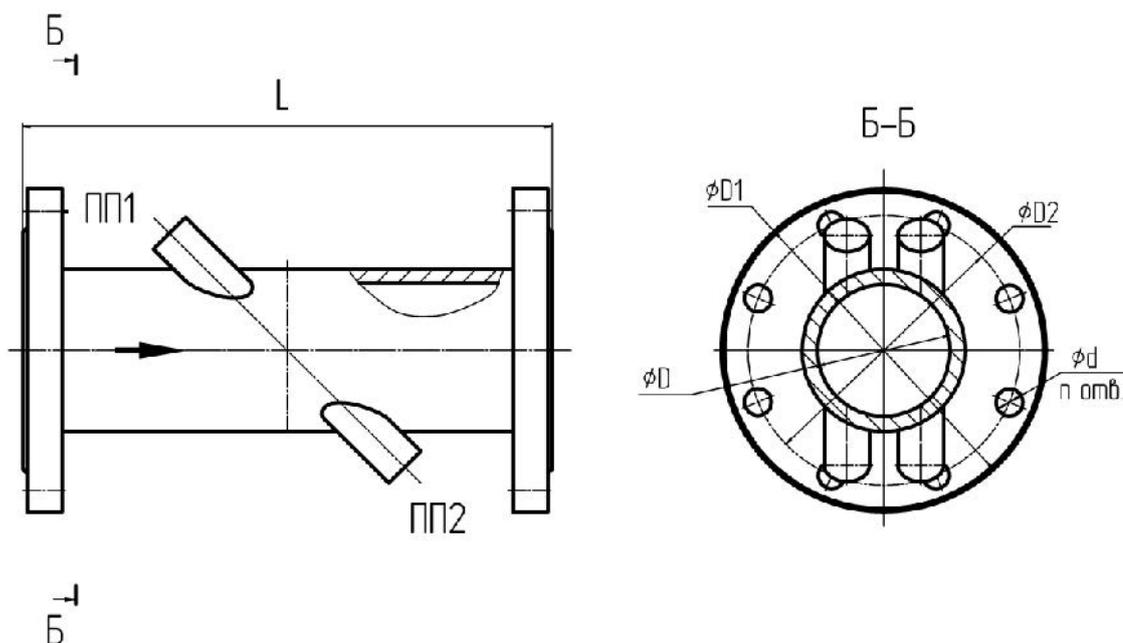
Габаритные и присоединительные размеры ИУ счетчиков исполнения 03 с параллельными акустическими базами
